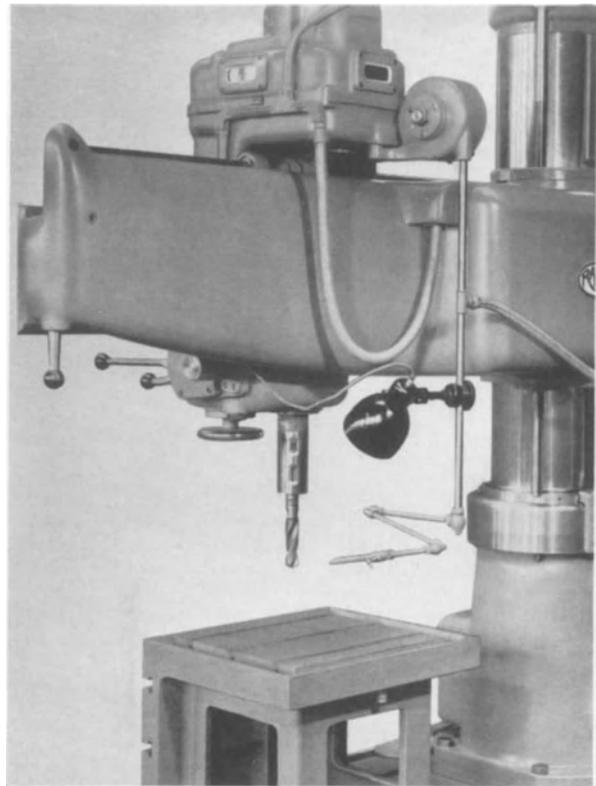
Einstellbare Werkplatzleuchte am Bohrschlitten
